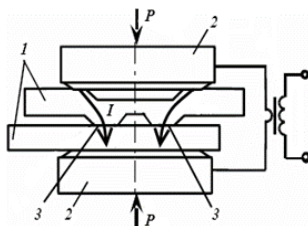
Принципиальная схема рельефной сварки:
